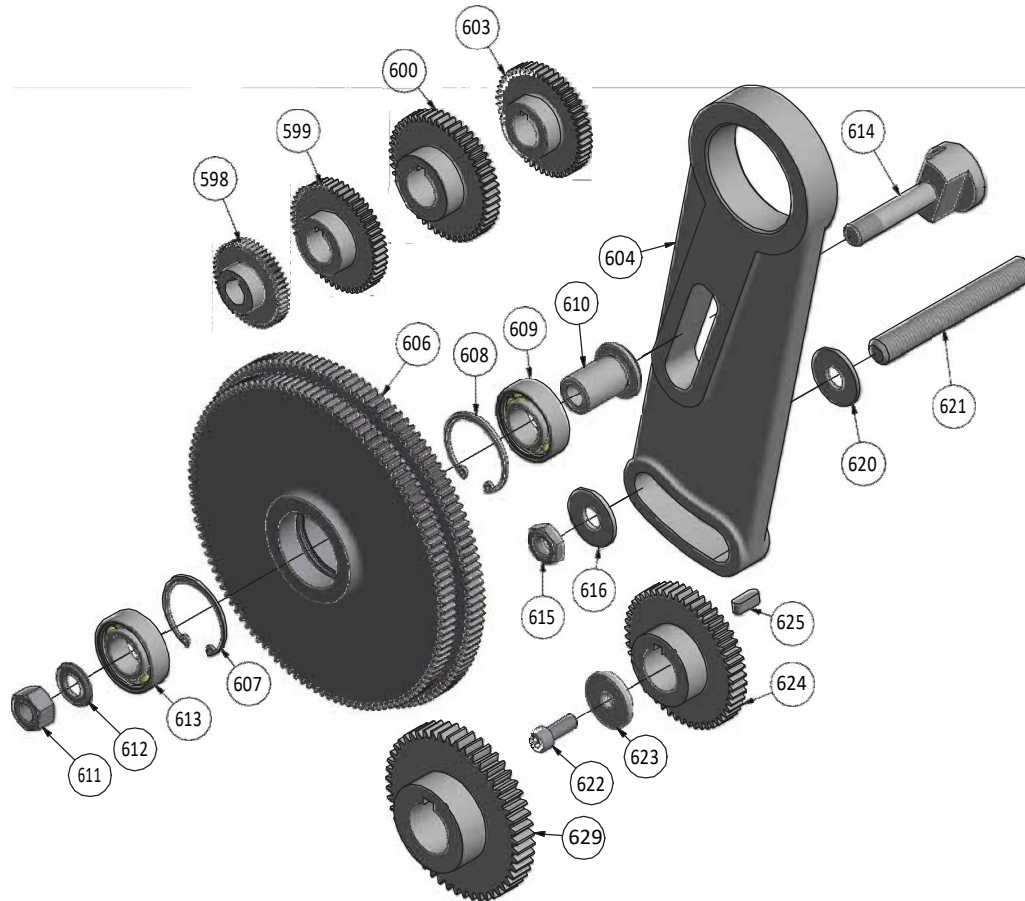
Wechselradgetriebe – Engranaje de cambio
